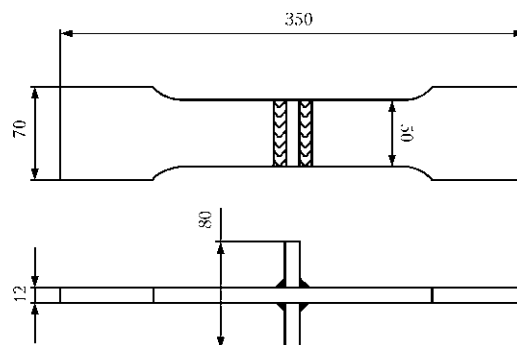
Схема образца сварного соединения стали 09Г2С
